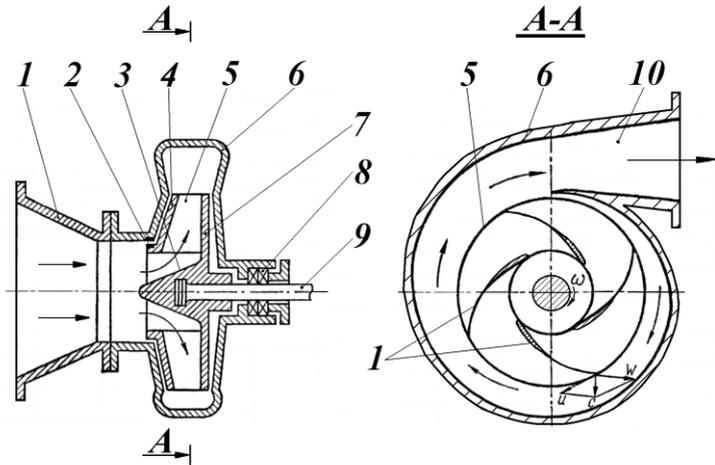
Схема центробежного насоса: 1-всасывающий патрубок; 2- уплотнение; 3- крепление рабочего колеса; 4 – передний диск; 5 – лопасти; 6 - спиралевидный отвод; 7 – задний диск; 8 – уплотнение вала; 9 – вал; 10- напорный патрубок
